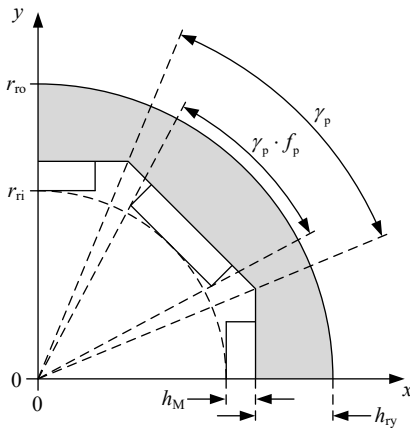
Parametrisierter Rotorquerschnitt mit massivem Rotorjoch und Oberflächenmagneten mit rechteckigem Querschnitt.
